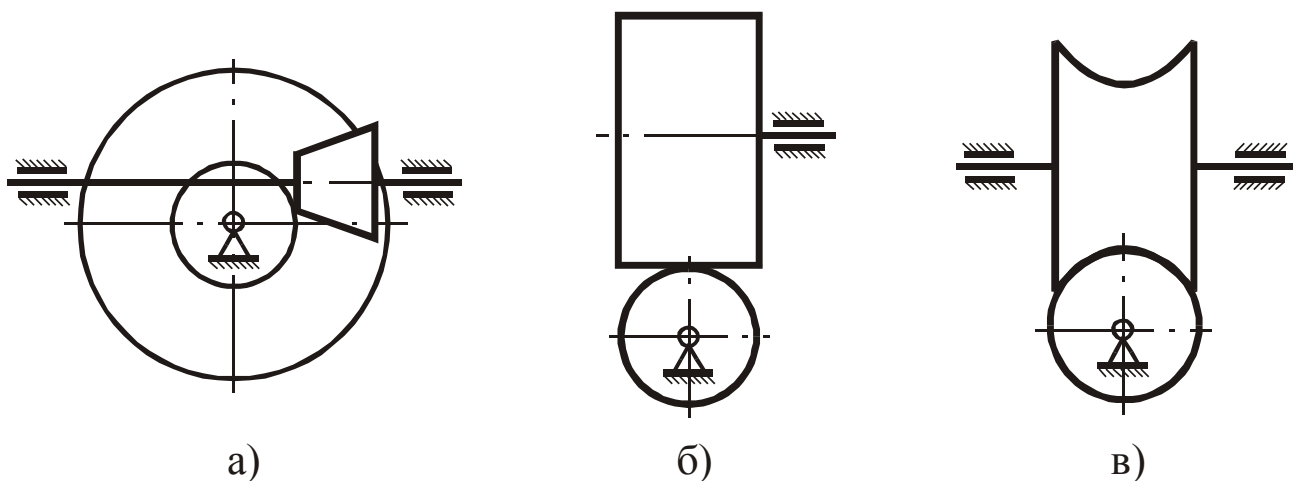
Гіперболоїдна зубчаста передача: а – гіпоїдна передача; б – гвинтова передача; в – черв'ячна передача
